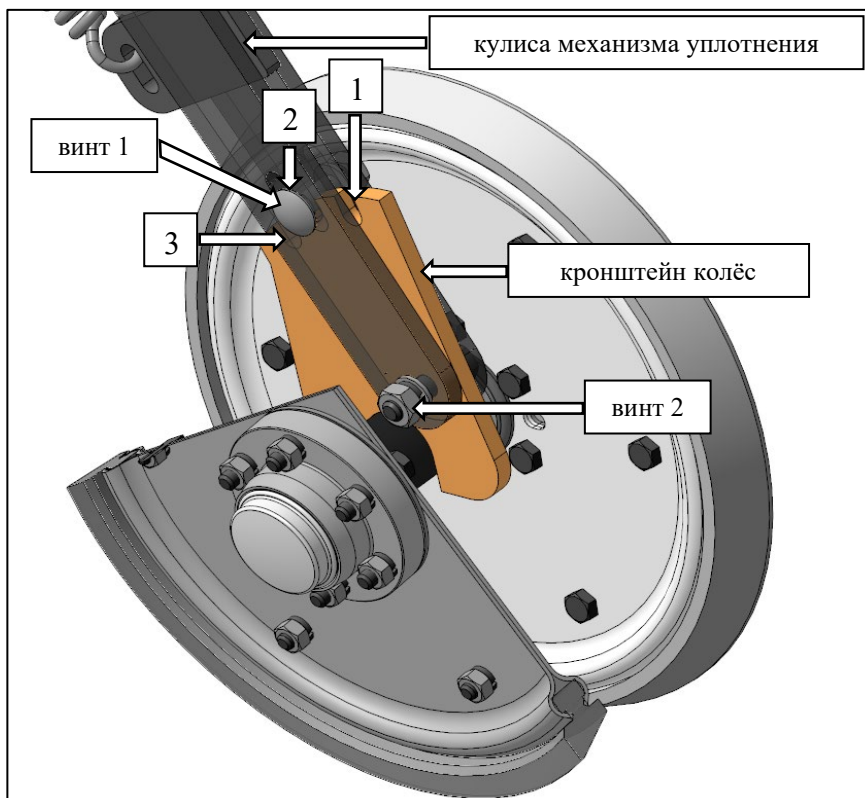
Механизм уплотнения (вид в разрезе),
